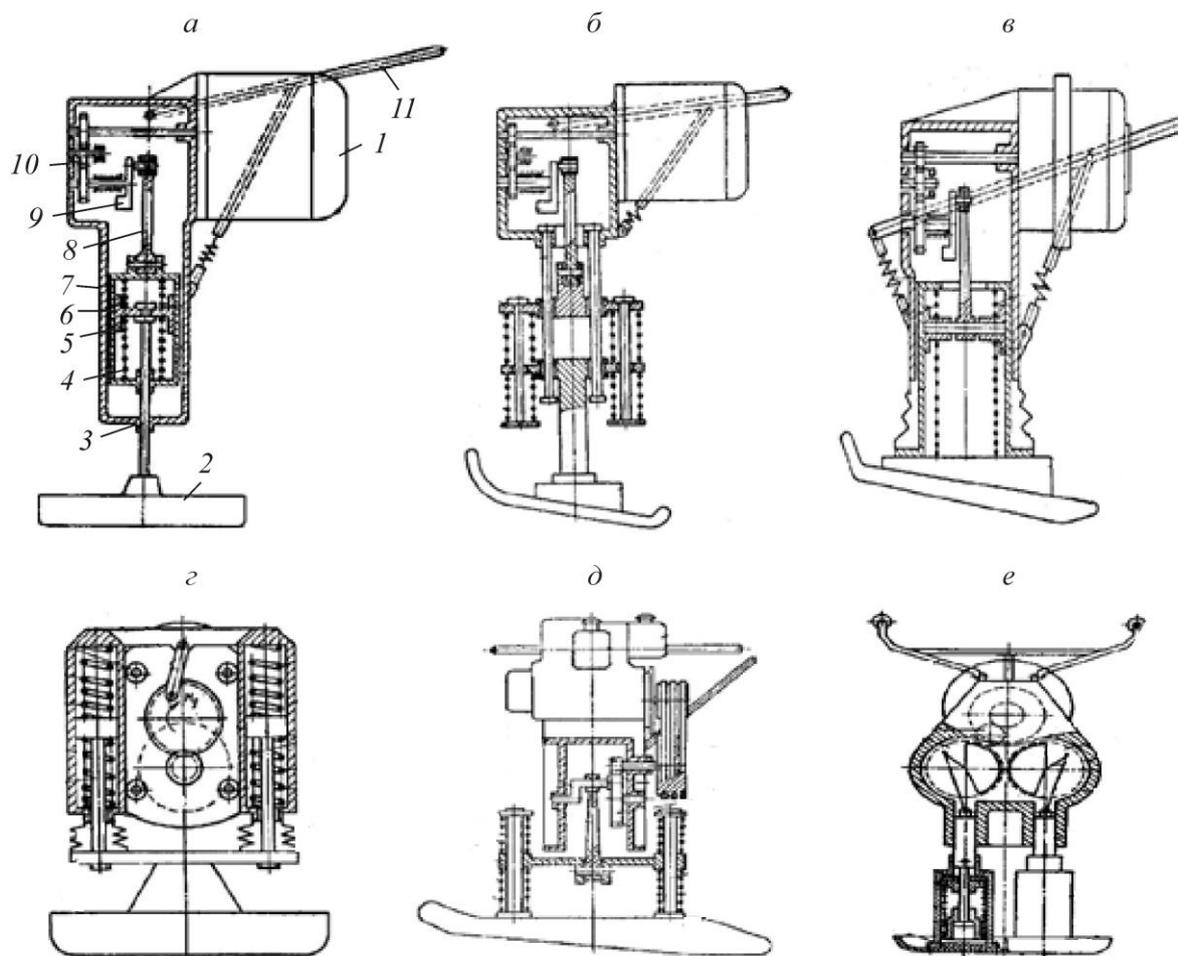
Конструкции зарубежных ручных трамбовочных машин: *а* — ручной трамбовки фирмы Wacker (ФРГ); 1 — электродвигатель; 2 — трамбуемый башмак; 3 — шток; 4 — нижний пакет пружин; 5, 6 — верхний пакет пружин; 7 — подвижный цилиндр; 8, 9 — кривошипно-шатунный механизм; 10 — одноступенчатый редуктор; 11 — рукоятка управления; *б* — электротрамбовки фирмы Allam (Великобритания); *в* — мототрамбовки BS-180 фирмы Wacker (ФРГ); *г* — грунтоуплотняющей машины BS-180 (ЧССР); *д* — мототрамбовки с пружинным ударным механизмом обозначения; *е* — трамбовки с динамическим гасителем колебаний
